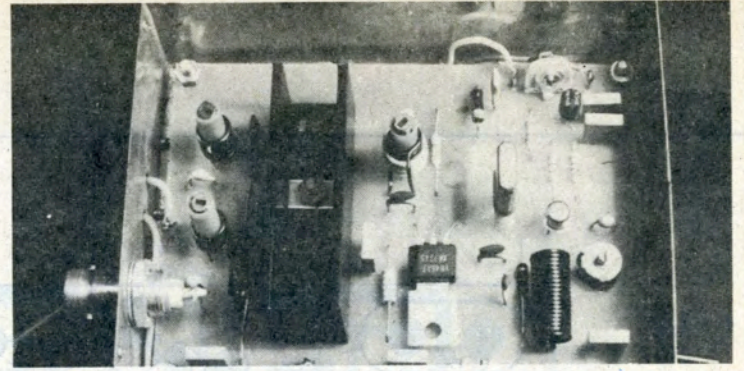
Photo F. — La platine HF vue du côté L1. Voir les arrivées S_M et S'.
